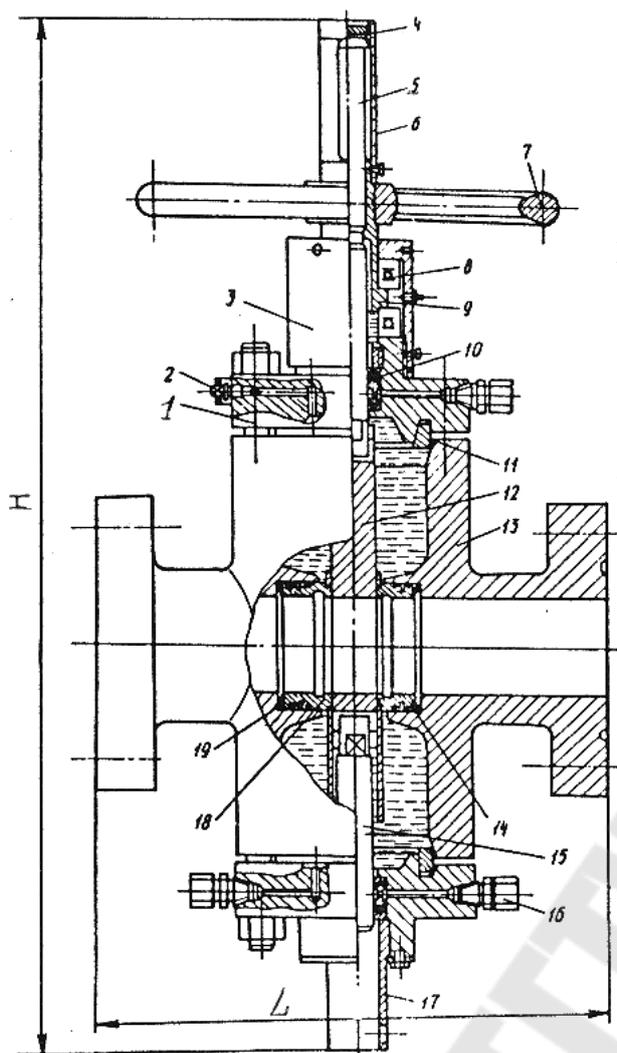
Задвижка типов ЗМС и ЗМС1 с ручным приводом:
